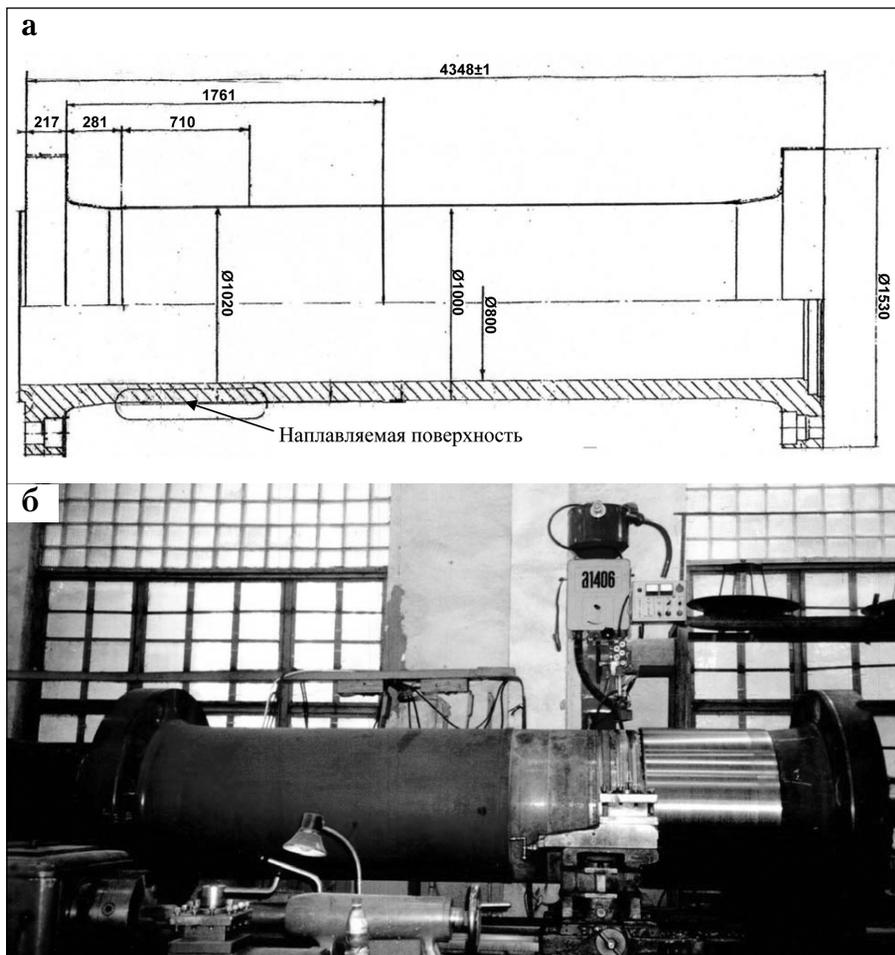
Эскиз вала гидротурбины (а) и процесс дуговой наплавки изношенной поверхности вала гидротурбины на установке на базе токарного станка ДИП-500 (б)
